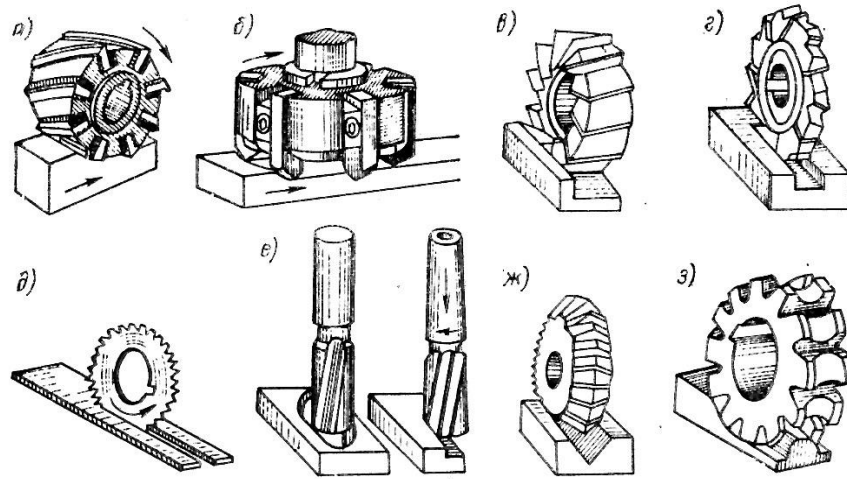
Характерные формы поверхностей, обрабатываемых фрезами: цилиндрическими (а); торцевыми (б); двухсторонними (в); дисковыми (г); прорезными и отрезными (д); концевыми (е); угловыми (ж); фасонными (з).
